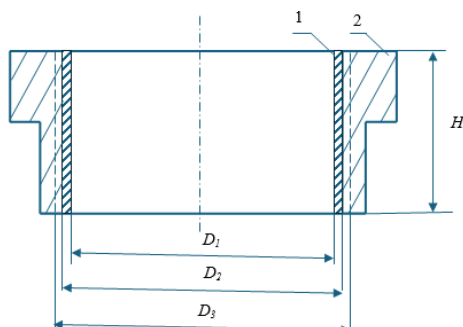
Схема нанесения покрытия на рабочую поверхность кольца: 1 - покрытие; 2 - корпус кольца
